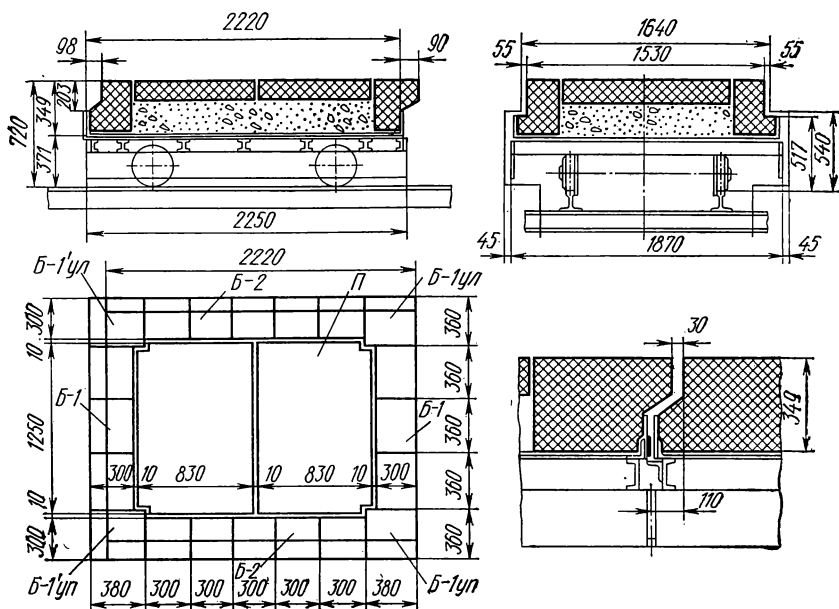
Раскладка блоков и плит футеровки вагонеток для туннельной печи по типовому проекту 409-21-5:
